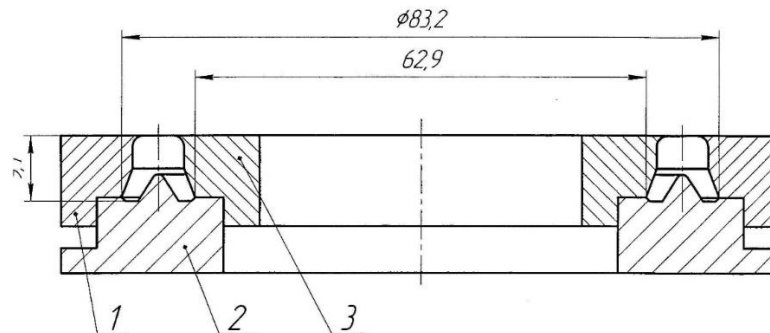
Литьевая форма для изготовления полиуретановых манжет (1- верхняя пластина; 2-нижняя пластина; 3-вкладыш)
